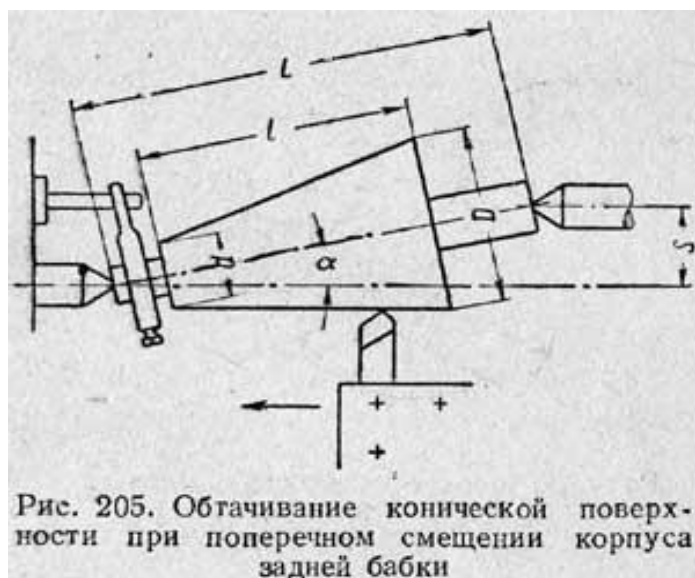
Обтачивание конической поверхности при поперечном смещении корпуса задней бабки
